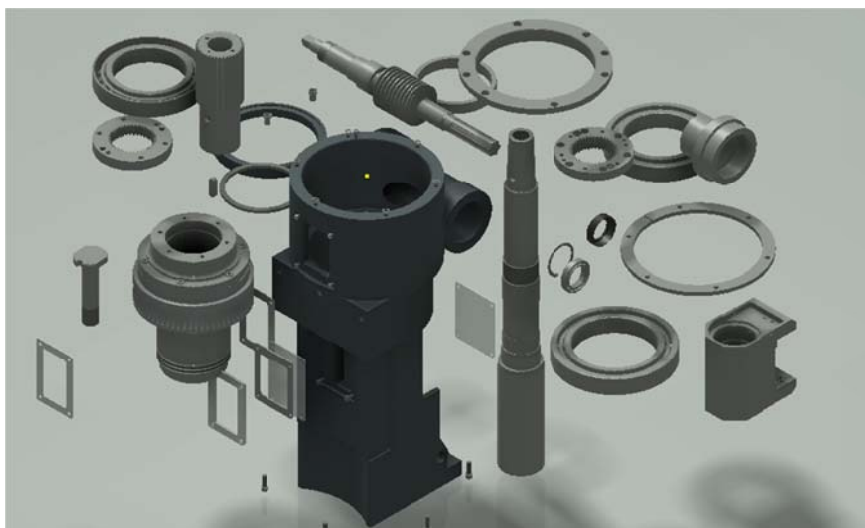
Суппорт полуавтомата зубофрезерного вертикального ВС-122
